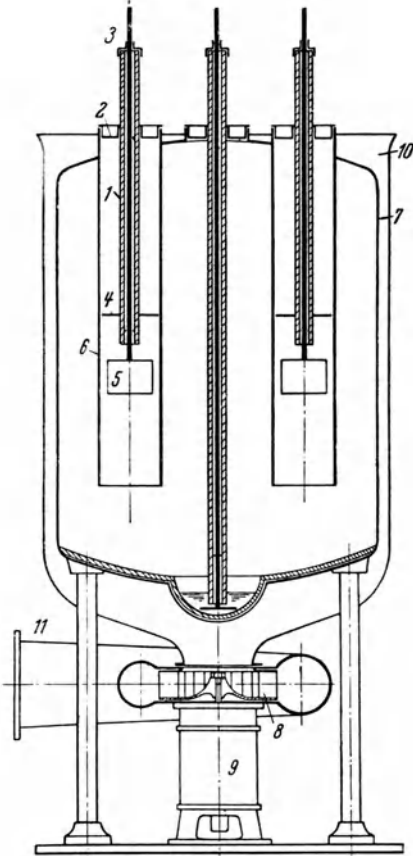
Schnitt durch einen mit Luft gekühlten, pumpenlosen Eisengleichrichter (J. Pintsch)
